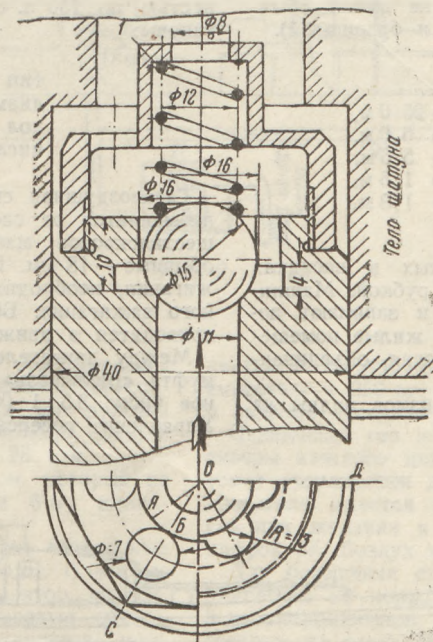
Невозвратный шариковый клапан, установленный на двигателе 6ЧР $\frac{42,5}{60}$:
